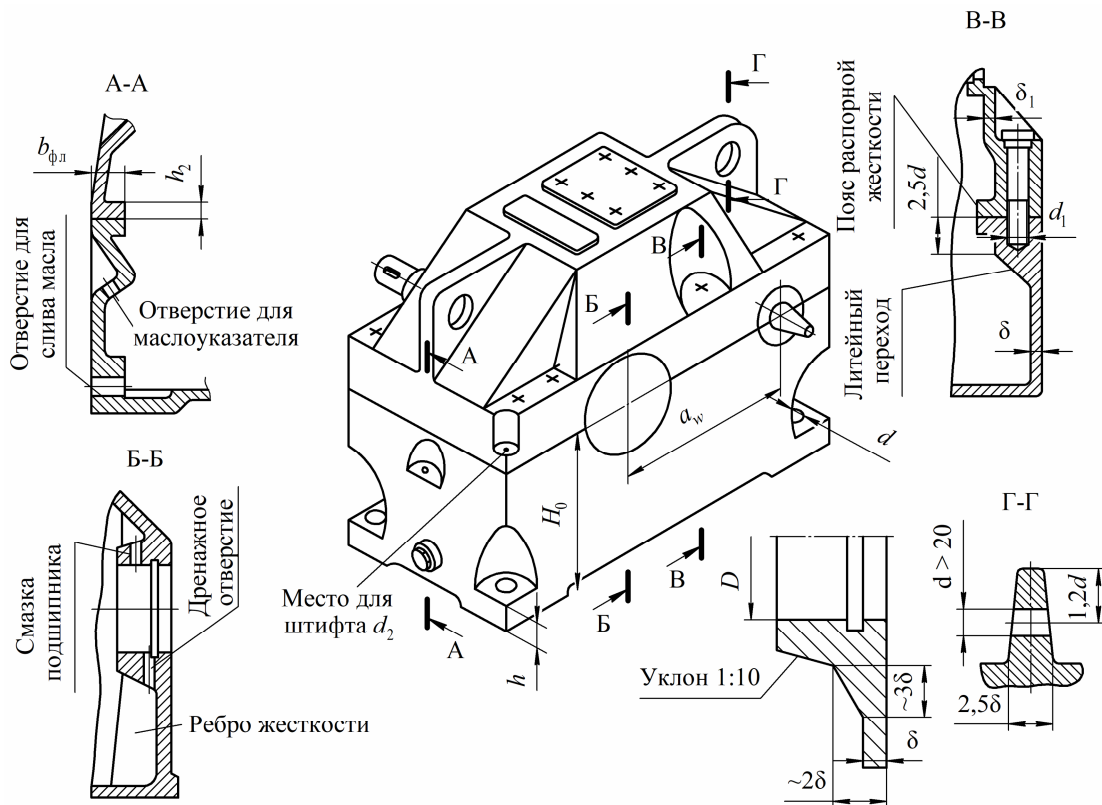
Корпус цилиндрического одноступенчатого редуктора
